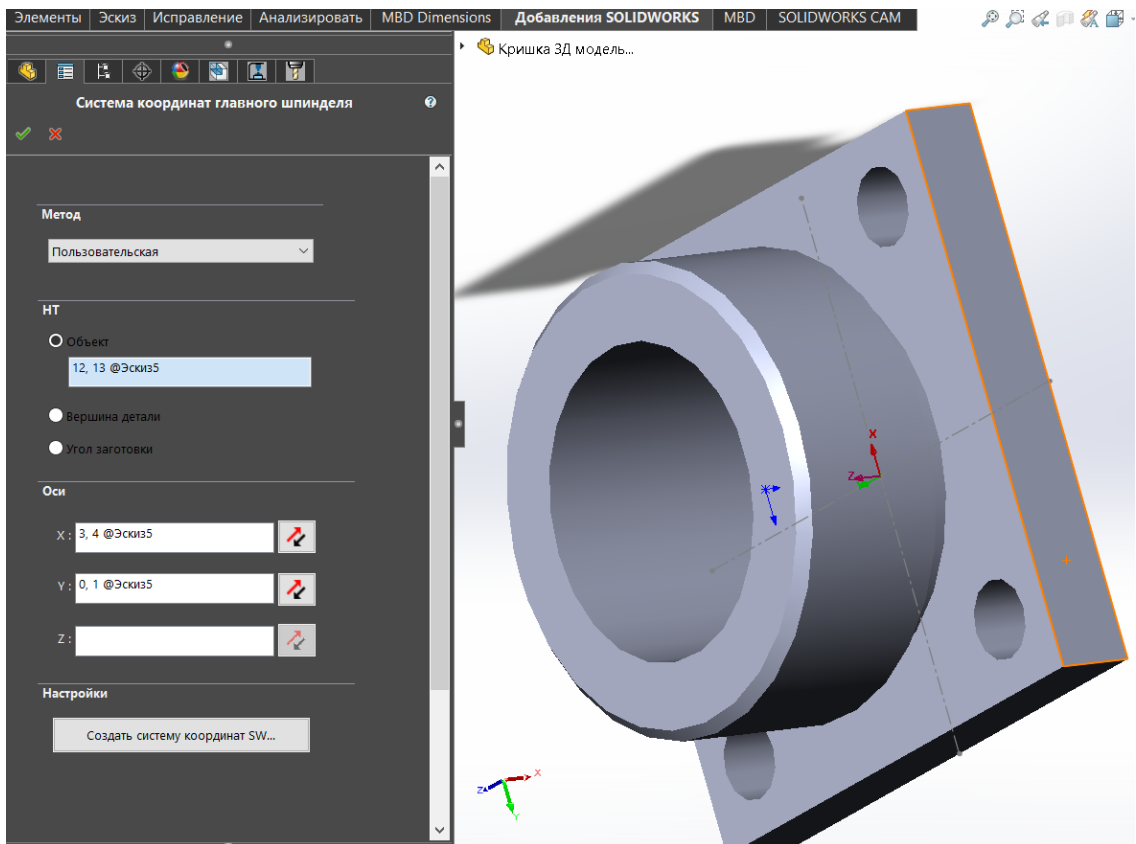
Встановлення системи координат шпинделя токарного верстата з ЧПК
